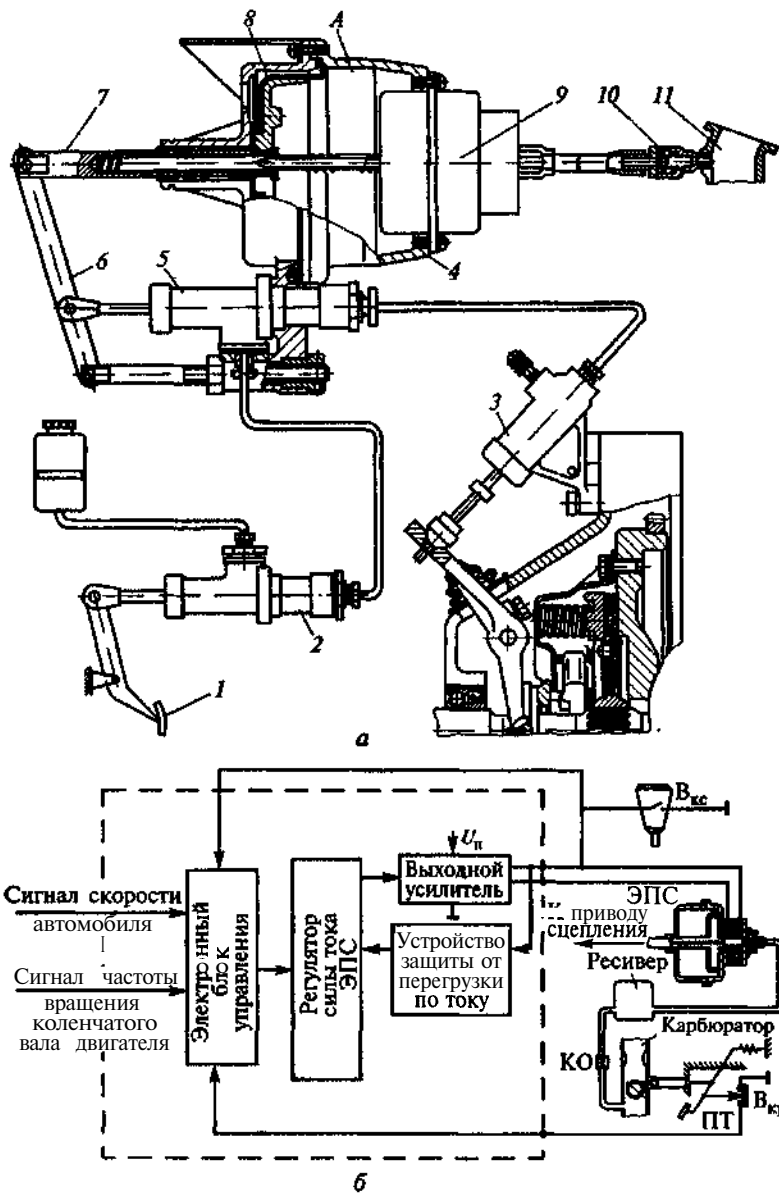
Исполнительный механизм привода выключения сцепления (а) и схема (б) его системы управления (разработка НАМИ): 1 — педаль; 2 и 3 — главный и рабочий цилиндры; 4 — сервокамера; 5 — гидроцилиндр; 6 — рычаг; 7 — шток; 8 — мембрана; 9 — электромагнитный клапан; 10 — обратный клапан; А — вакуумная полость, 11 — впускной трубопровод; ЭПС — электропривод сцепления; КО — обратный клапан; ПТ — педаль тормоза; В_{кр} — микровыключатель; В_{кс} — кнопка выключения сцепления; U_п — напряжение питания
